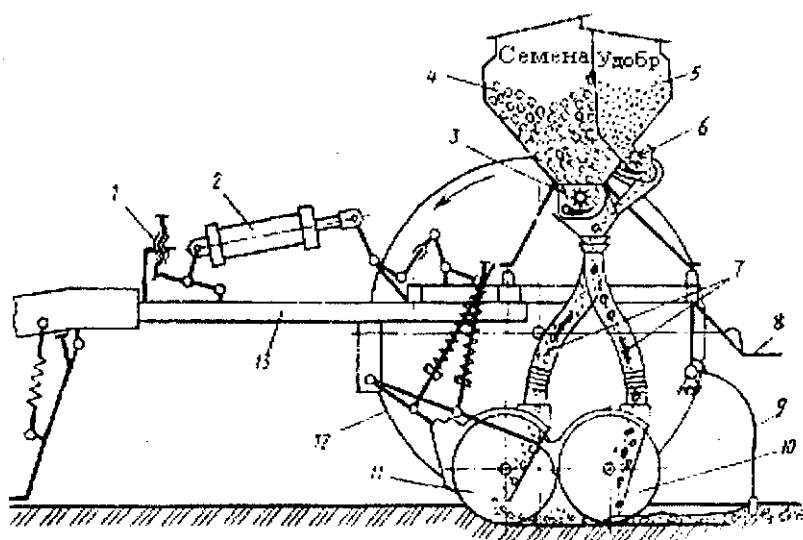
Технологическая схема зернотуковой сеялки СЗ-3.6: 1 и 14 - винтовой механизм; 2-гидроцилиндр; 3 и 6 - высевальные аппараты; 4 и 5 - ящик; 7-семяпровод; 8-подножная доска; 9-загортач; 10 и 11 - сошник; 12-опорно-приводное колесо; 13-рама.
